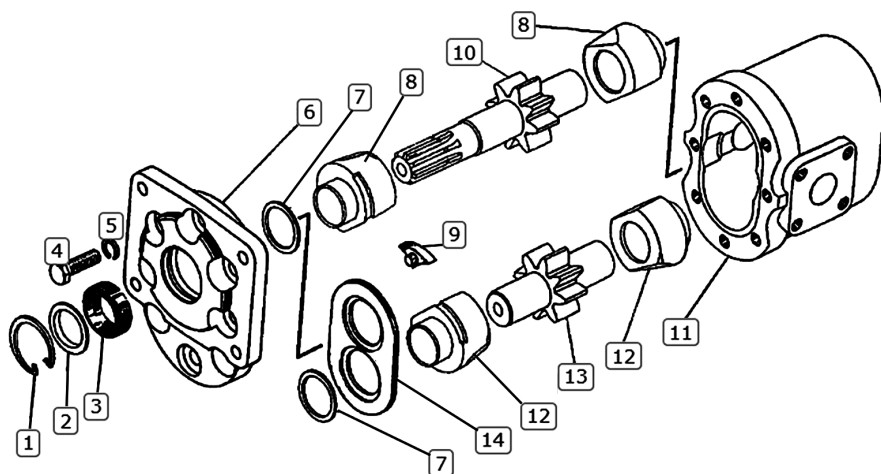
Детали и сборочные единицы шестеренного насоса двигателя автомобиля:
